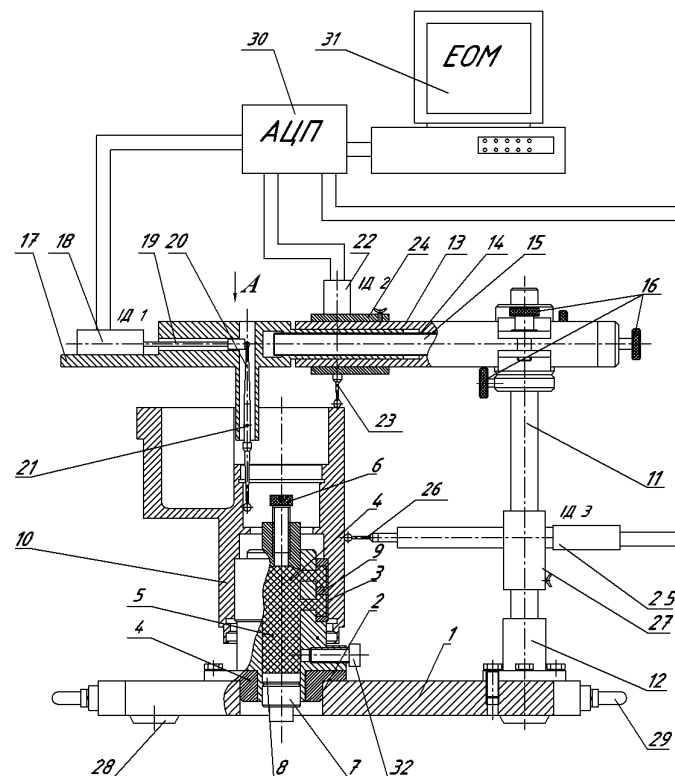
Контрольний пристрій для заміру параметрів корпусних деталей
